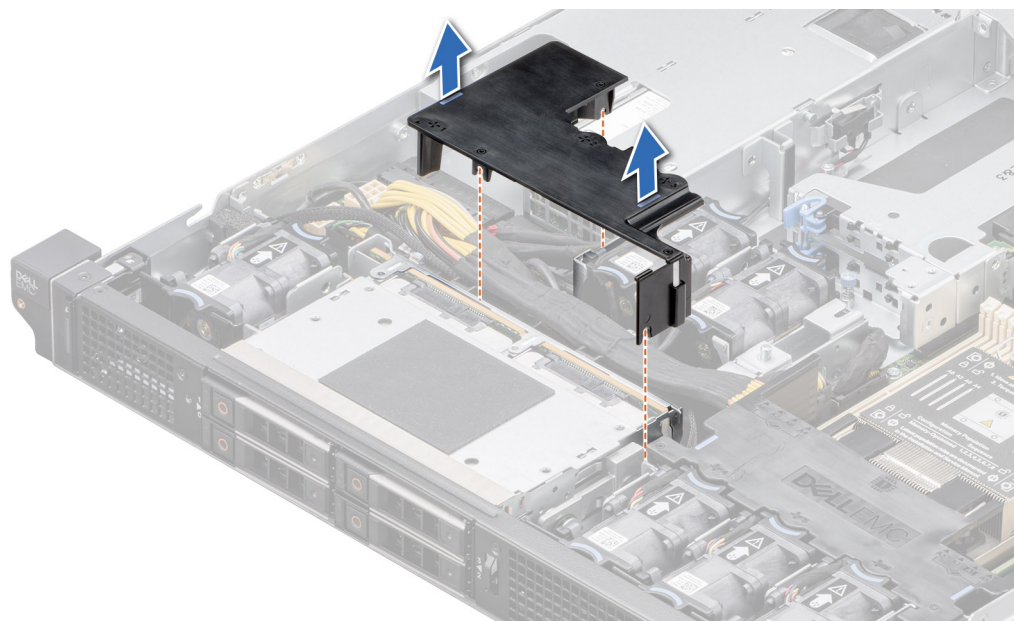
Entfernen des PCI-Kühlgehäuses
